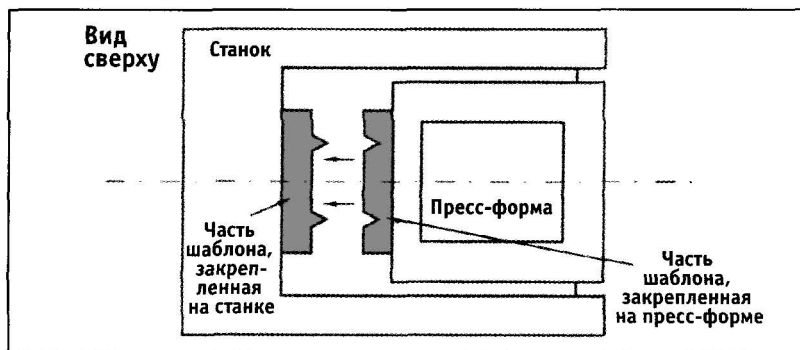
Центрующий шаблон позволяет точно установить пресс-форму или деталь
